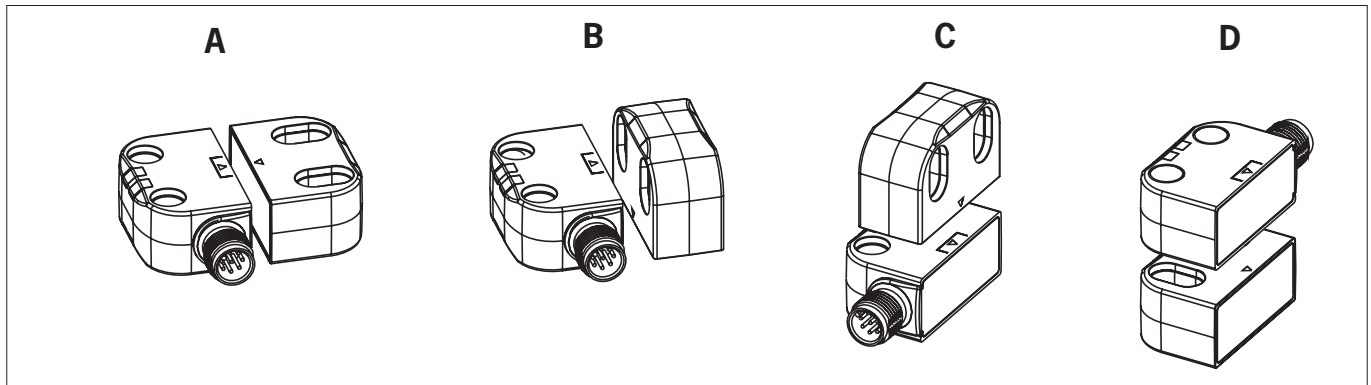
Zulässige Einbaupositionen für Betätiger CES-A-BTN-C07-... und A-FLX-C07-04-...: Pfeilrichtung auf dem Gerät beachten.
